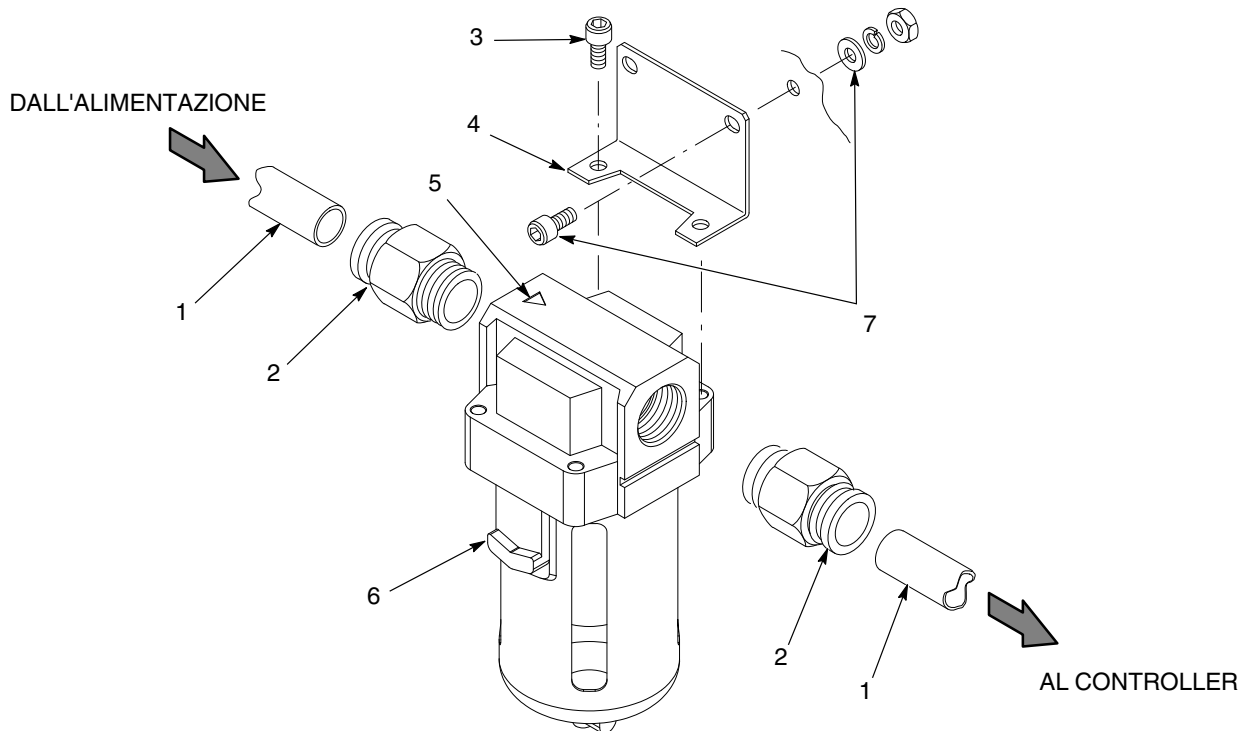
Installazione del filtro dell'aria - Sistemi con montaggio su rotaia e parete
